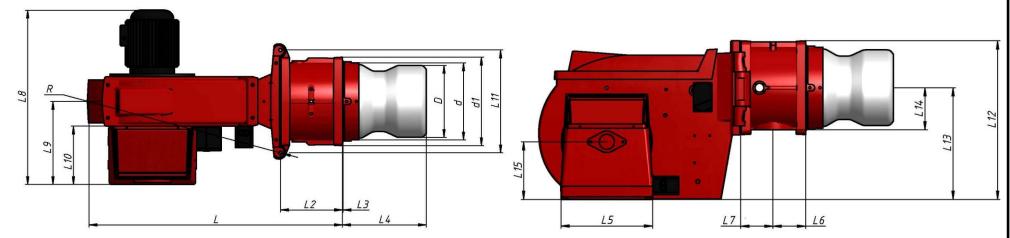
Габаритные и присоединительные размеры горелок ГГБ-5,4...ГГБ-10,5
